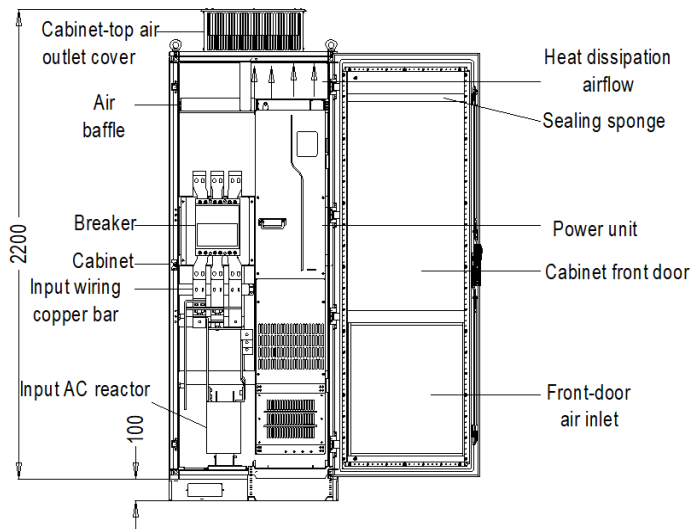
Схема монтажа ПЧ в шкафу с прямым выпуском 41
